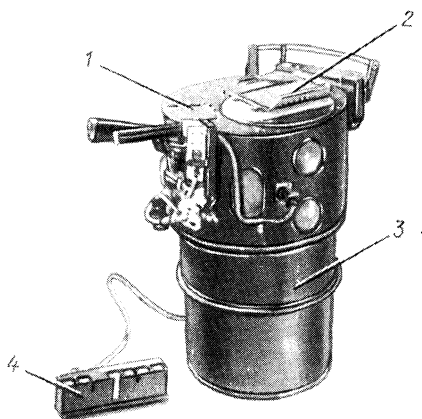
Установка для сварки и резки в космосе "Вулкан":
